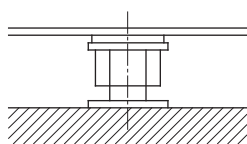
Vis de réglage de niveau sur la surface de fondation
